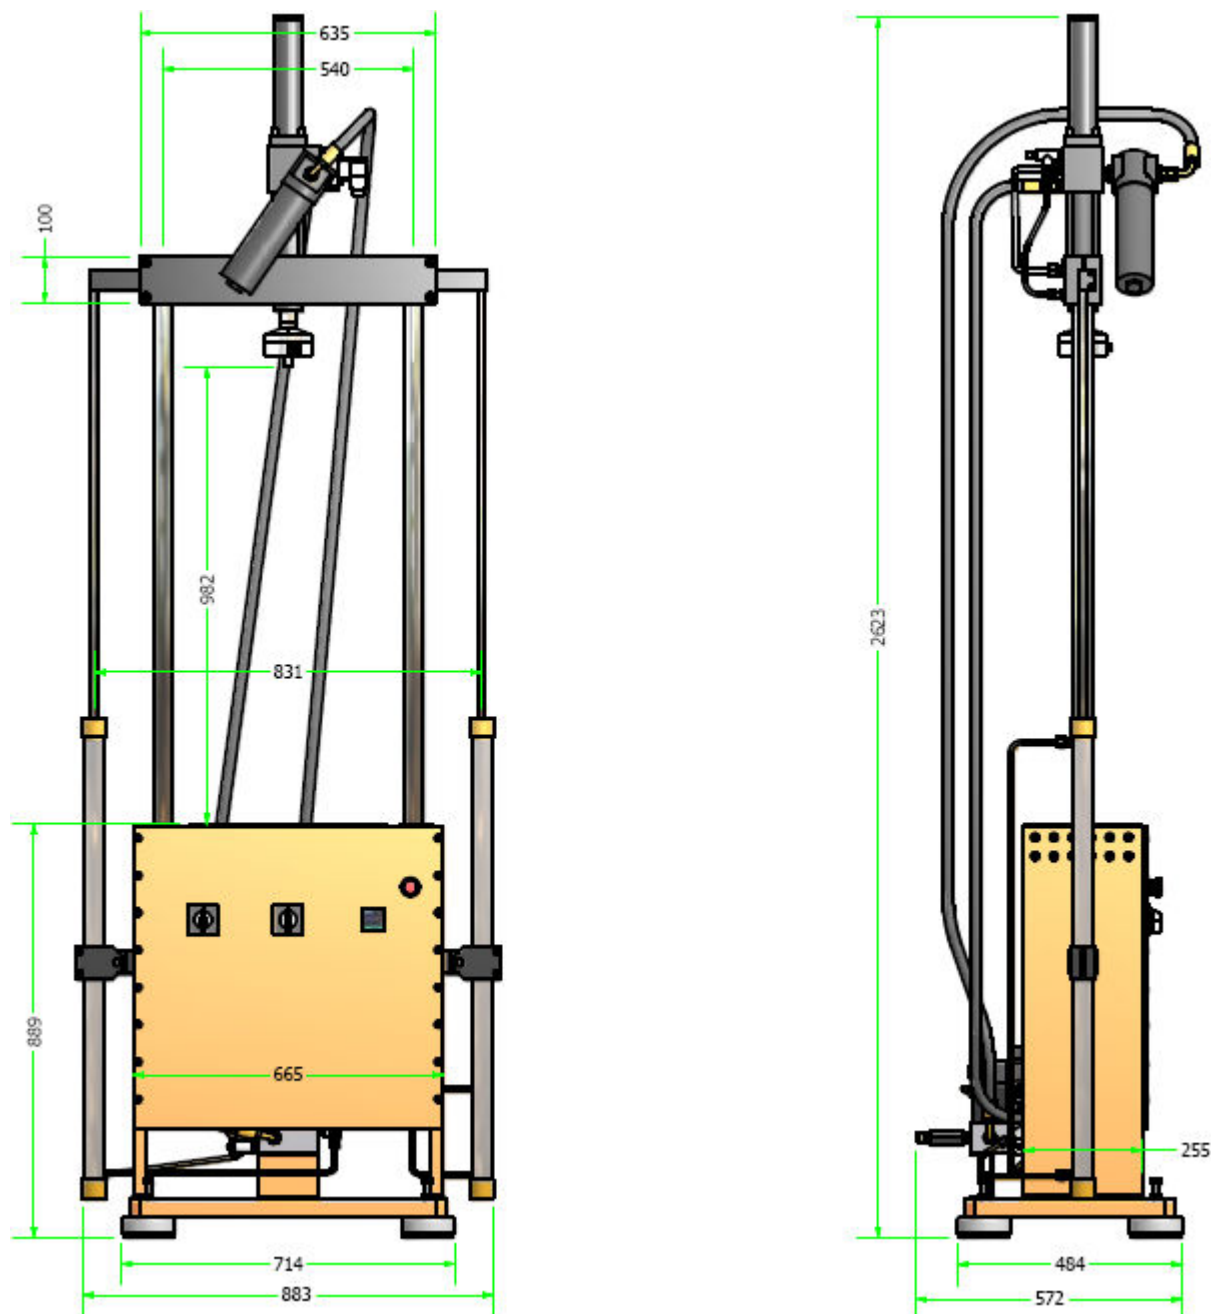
Dimensões principais da máquina de ensaio de 2000 kg
